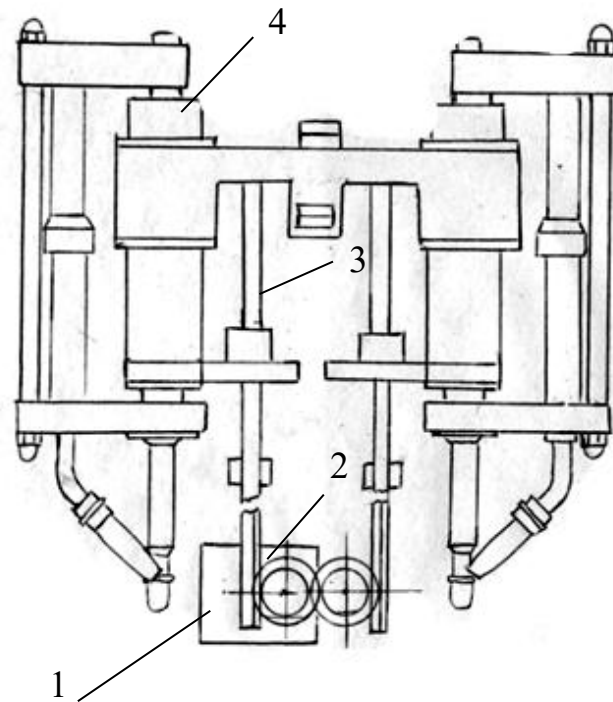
Механізм опускання зварювальних головок з рейковою передачею
